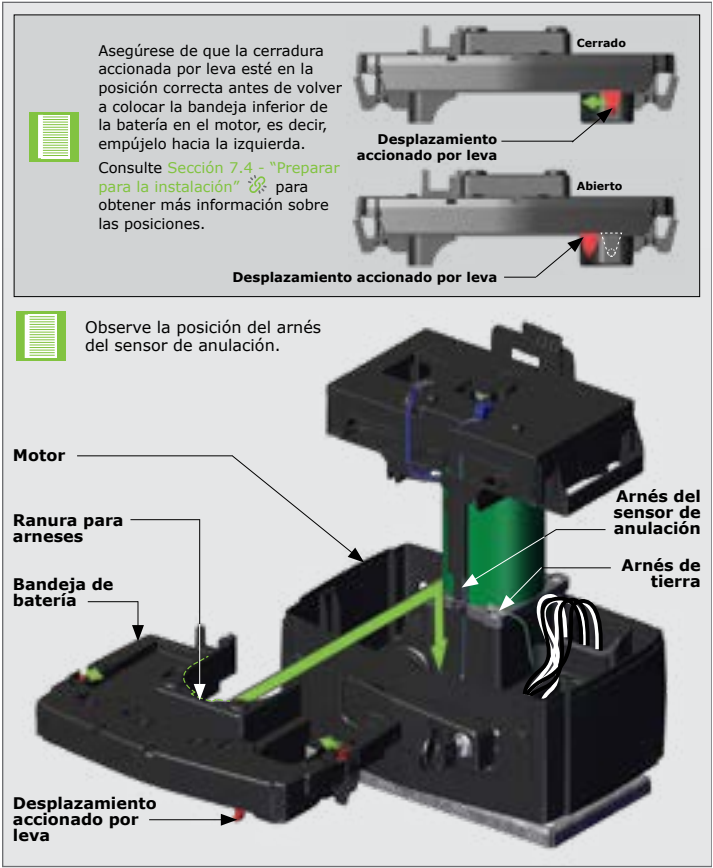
PONER LA BANDEJA INFERIOR DE LA BATERÍA
